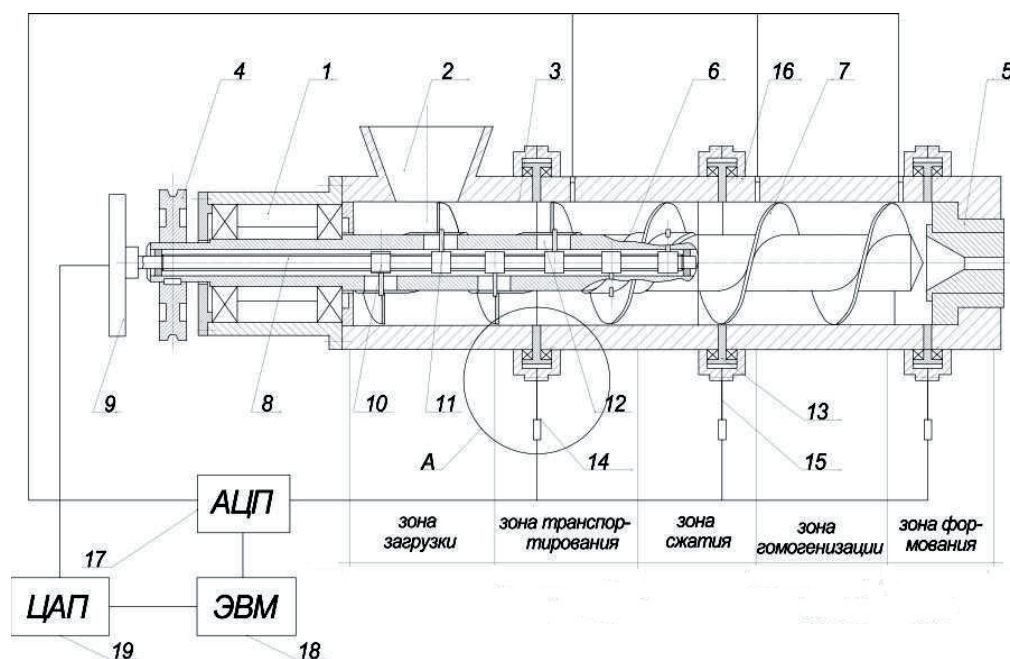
Схема установки с автоматическим контуром управления для экструдирования кормовых продуктов: 1 – подшипниковый узел; 2 – загрузочная воронка; 3 – разъемные корпуса шнековой камеры; 4 – привод; 5 – формирующая головка; 6 – шнек; 7 – витки шнека; 8 – резьбовой вал; 9 – приводной механизм; 10 – втулки с установленными пальцами; 11, 12 – направляющие, выполненные в теле шнека; 13 – цилиндрическая вставка; 14 – тензодатчики; 15 – гибкие элементы; 16 – датчики температуры; 17 – аналого-цифровой преобразователь; 18 – компьютер; 19 – цифро-аналоговый преобразователь
